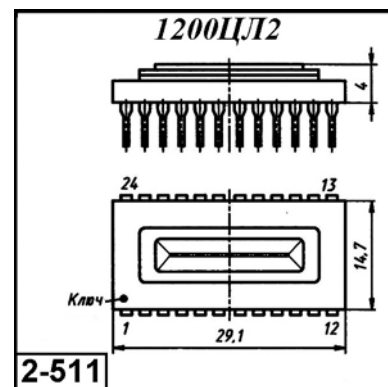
Внешний вид и габаритные размеры 1200ЦЛ2
